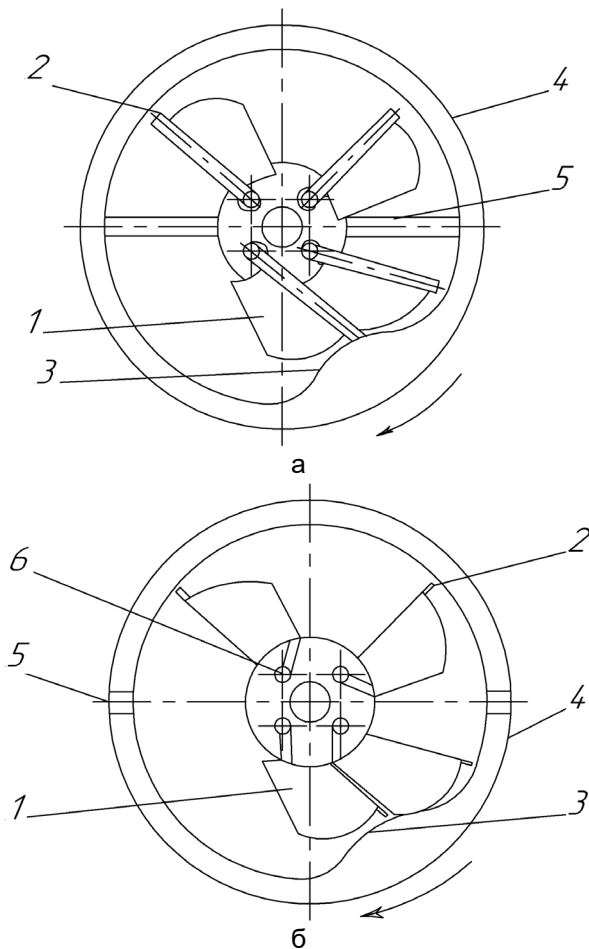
Схема удосконаленого відцентрового робочого органу з активними лопатками: а – вид зверху; б – вид знизу; 1 – лопатка; 2 – палець; 3 – випуклість; 4 – шайба; 5 – стрижень; 6 – важіль.
